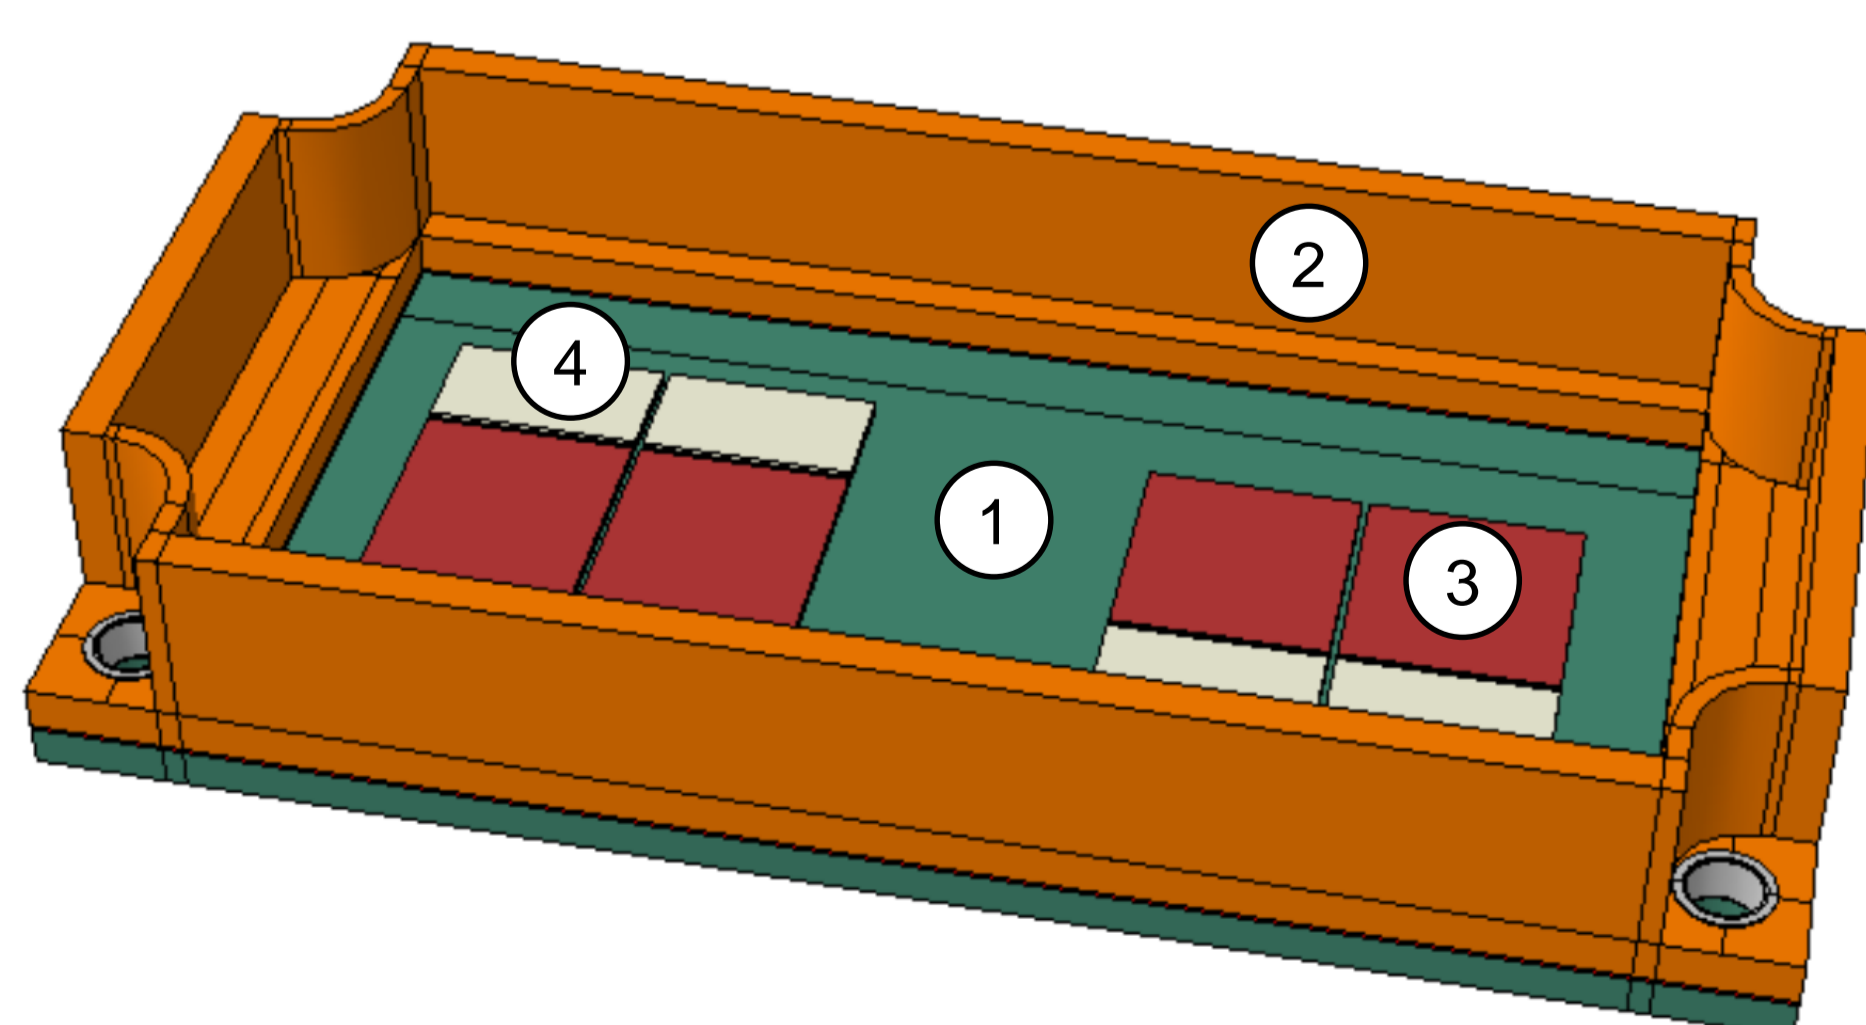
Konzepte für die Befestigung des LoPak Moduls auf dem Kühler
